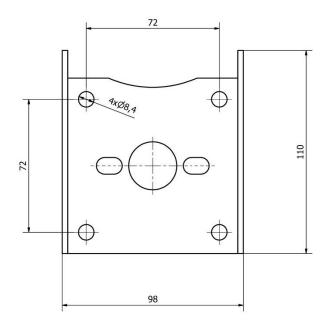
Индикатор расходомера с креплением. Габаритные размеры
